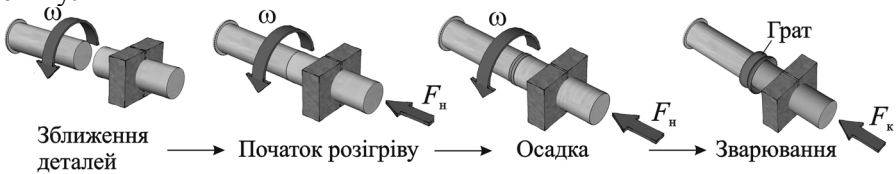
Етапи конвекційного зварювання тертям
